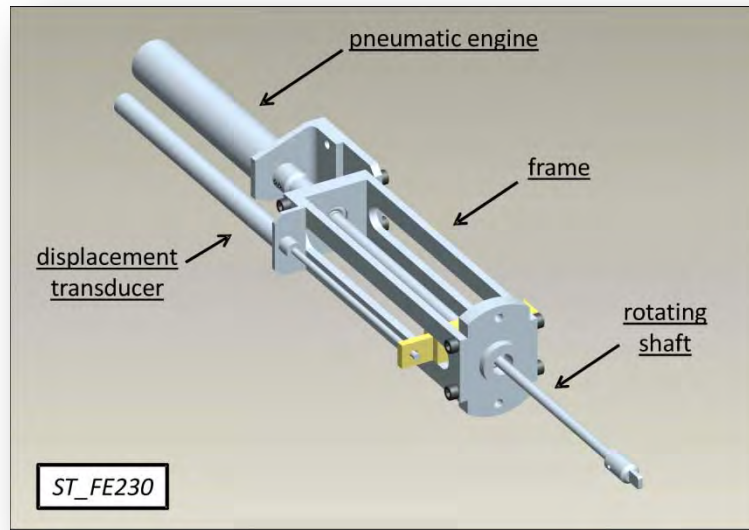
Il sistema a motore pneumatico dell'elettrodo estrattore ST_FE230.
